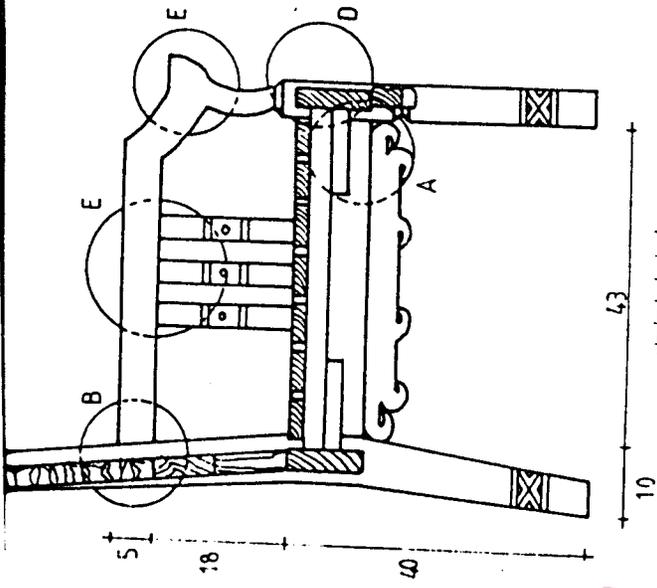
DETAIL ORNAMEN WATON MEJA 3kg. DEPAK
